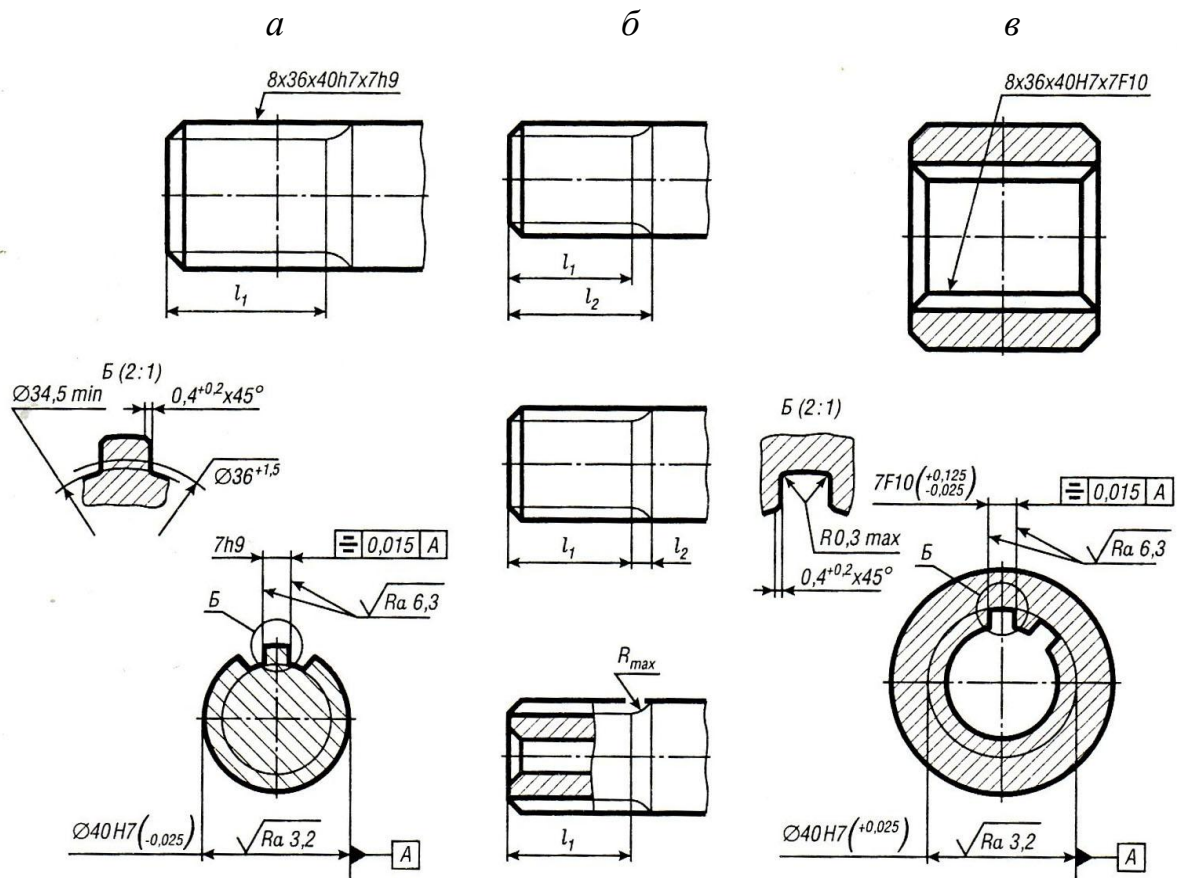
Чертежи деталей с прямоугольным профилем: *а* – шлицевой вал; *б* – варианты задания длин зубьев полного профиля и сбега; *в* – шлицевая втулка (отверстие)
